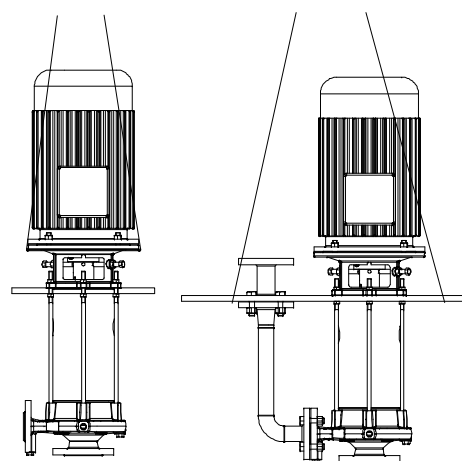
Транспортировка агрегата без / с защитной плитой до типоразмеров двигателя 160
